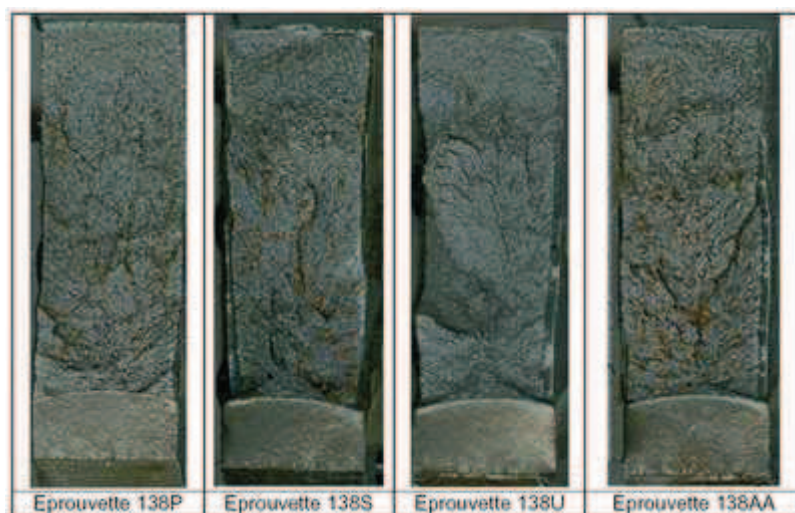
Macrographies des faciès de rupture - éprouvettes CT testées à -100°C
